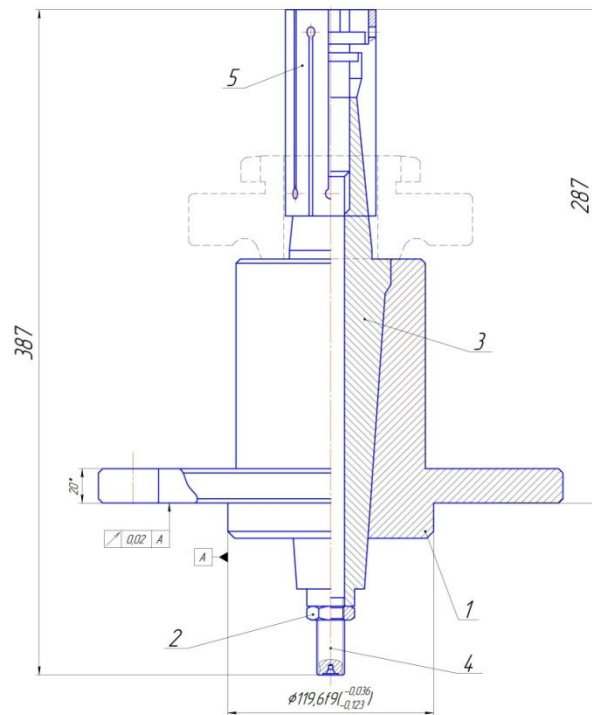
Приспособление для зубодолбежного станка 5М150
